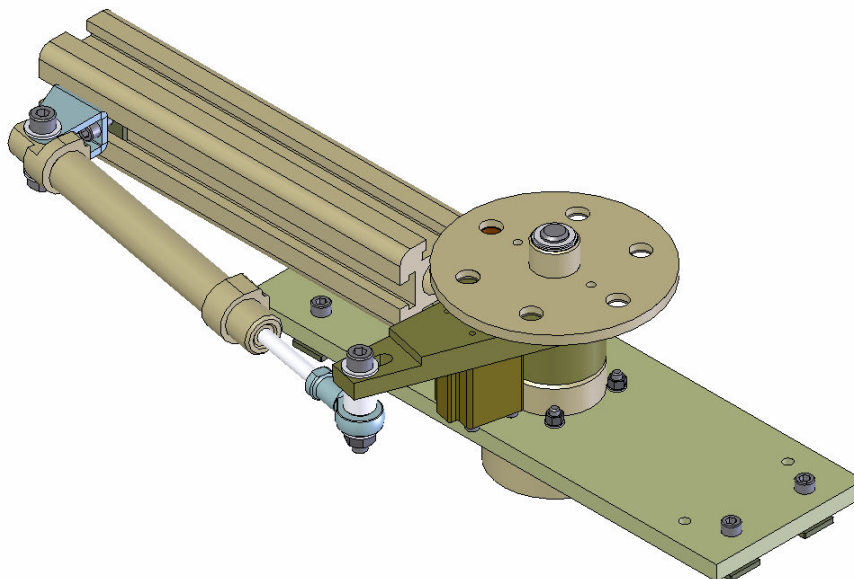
Vue d'ensemble du plateau indexeur en position assemblée.
